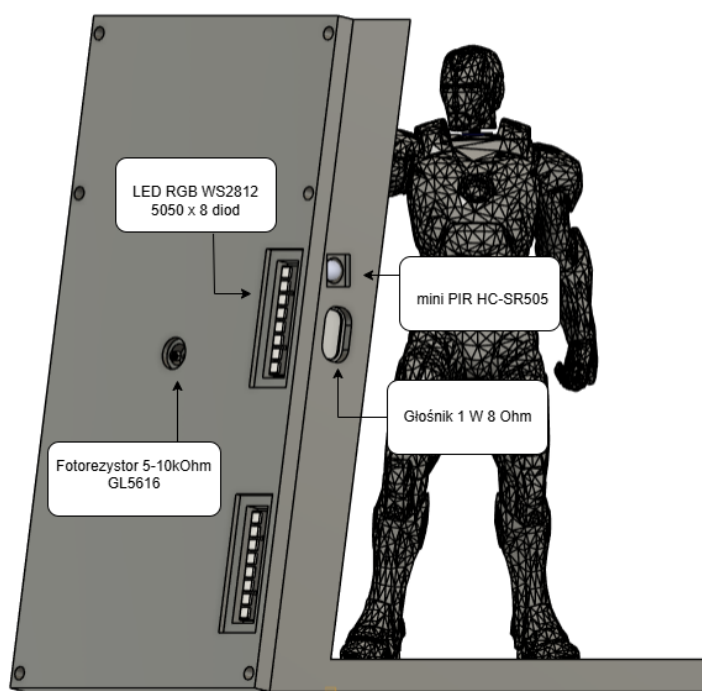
Widok modelu 3D z objaśnieniem elementów projektu (1)
